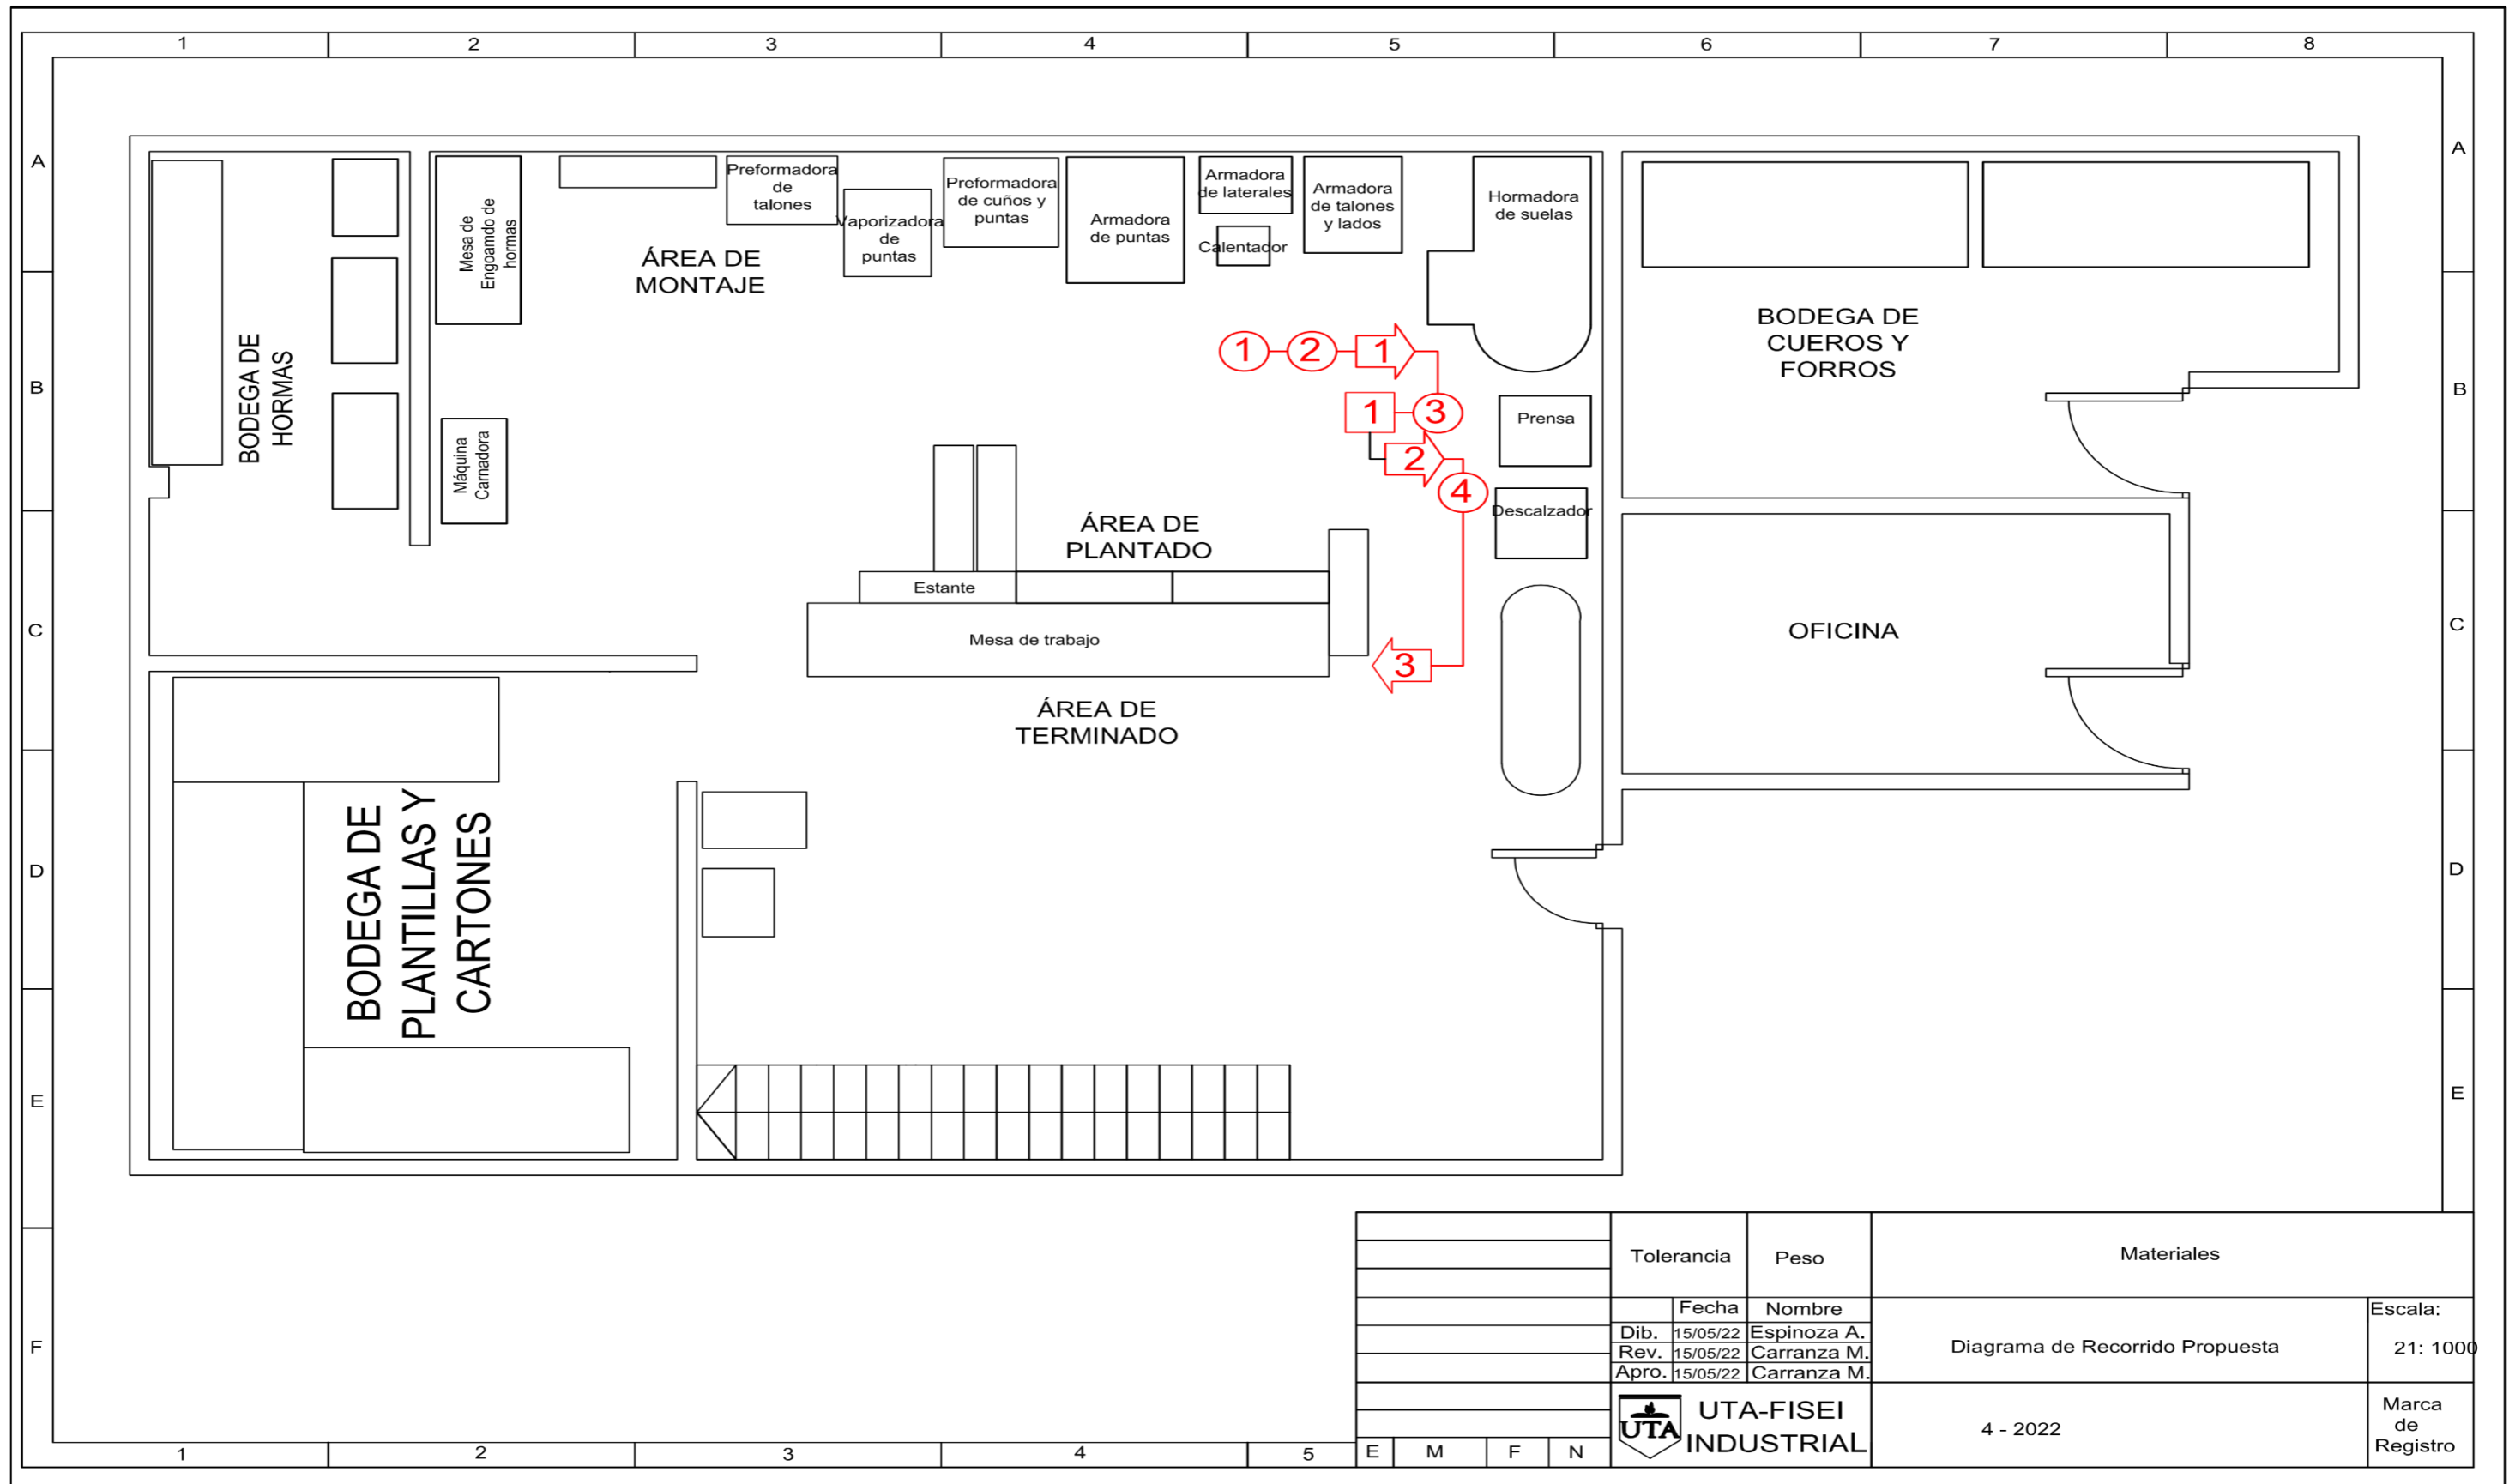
Diagrama de recorrido propuesta -Área de Plantado
